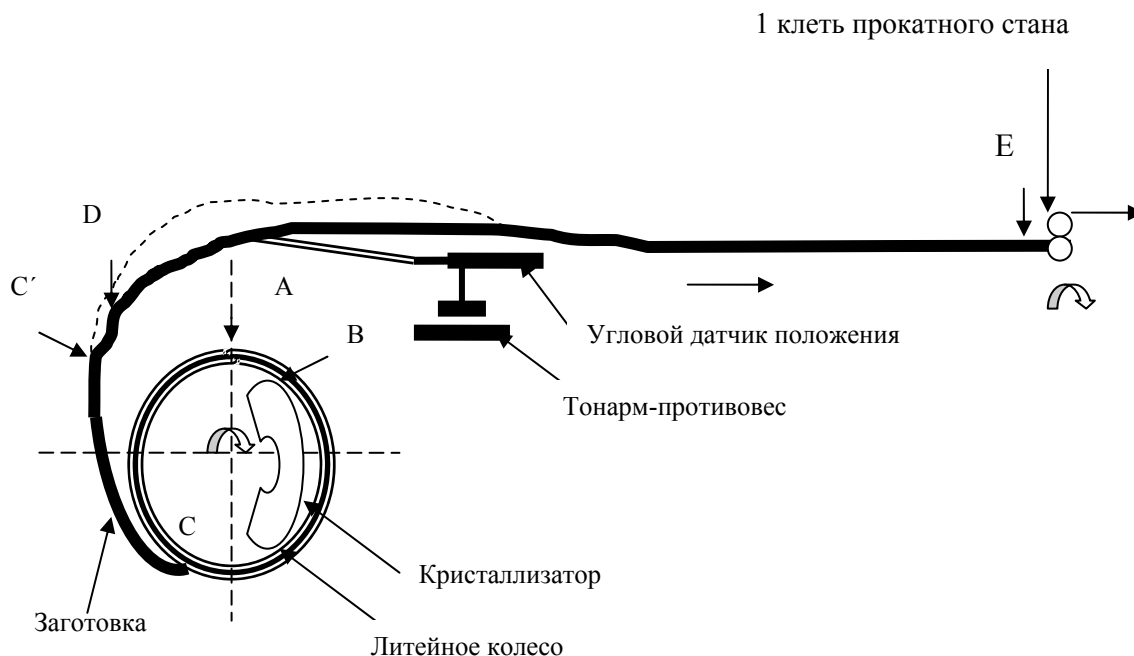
Схема формирования алюминиевой заготовки при литье
